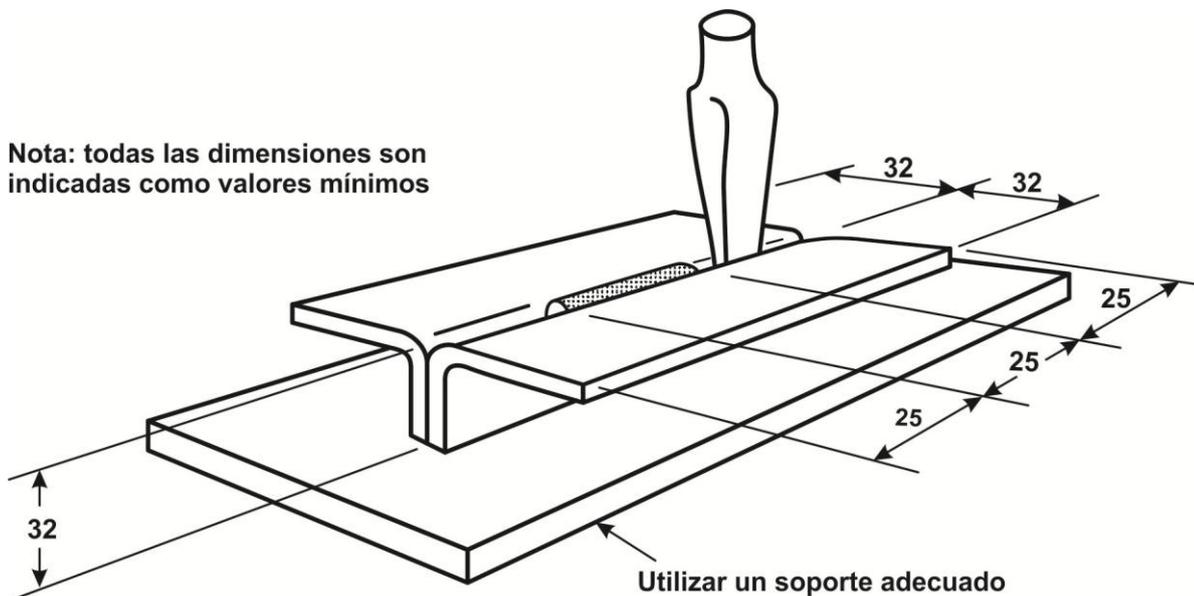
c). Esquema de ensayo para soldadura con junta acampanada en V.
